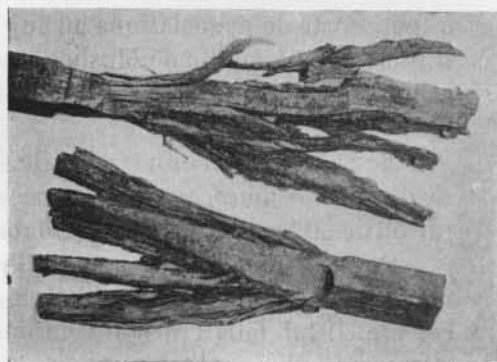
Barre carrée de fer du Yorkshire de première qualité (best-best), forgée au rouge ordinaire, au-dessous de la température de soudage.
